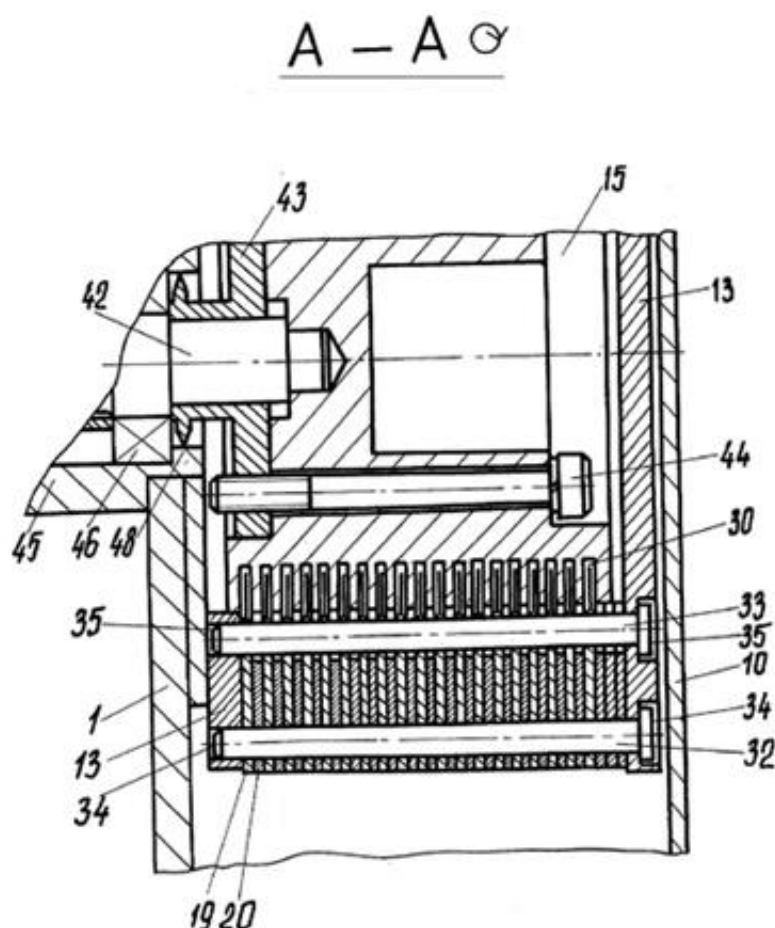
Розріз ножового барабана з розміщеними лезами ножів в канавках барабану машини для різання овочів і фруктів марки А9-КИП.
